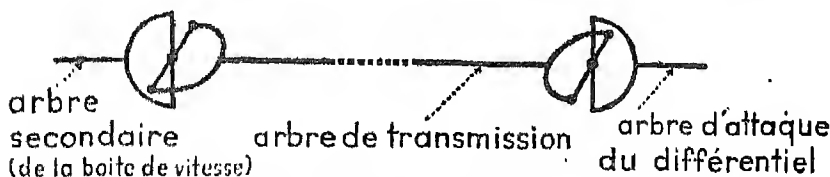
Schéma de l'arbre de transmission. Il porte un joint de Cardan à chacun de ses bouts. Pourquoi ?
